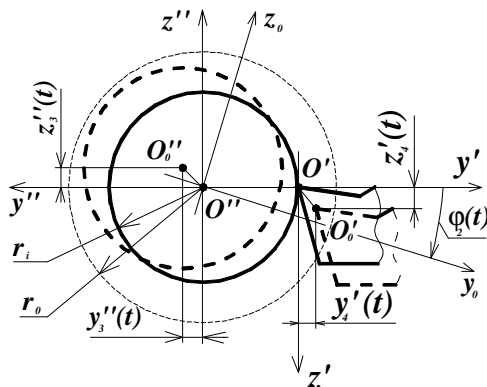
Схема формоутворення під час токарної обробки, де $O''O_0''$ - поточне положення осі деталі; $O'O_0'$ - поточне положення вершини інструменту; r_0 – радіус заготовки; r_i – заданий радіус оброблюваної поверхні деталі
